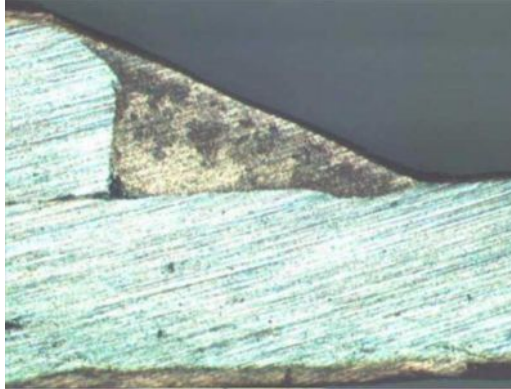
Îmbinare sudobrazată laser-MIG prin suprapunere [88]
